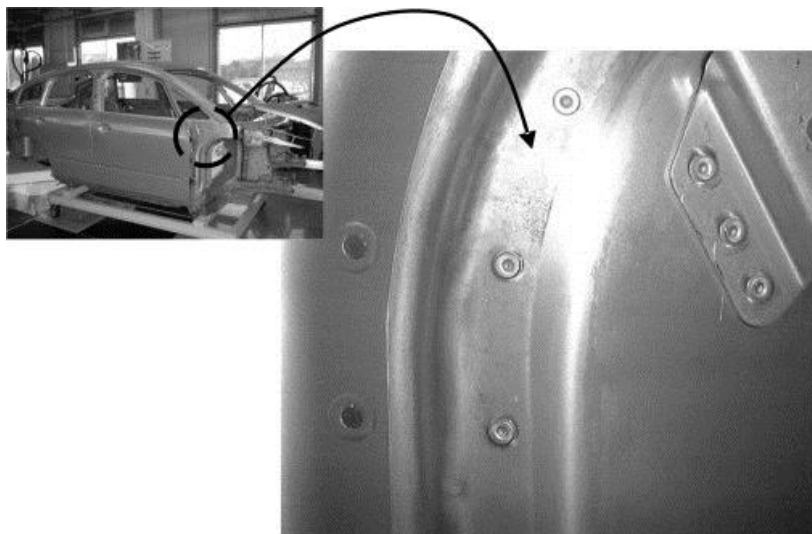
Détail d'une caisse en blanc assemblée par des rivets auto-poinçonneurs [91]
